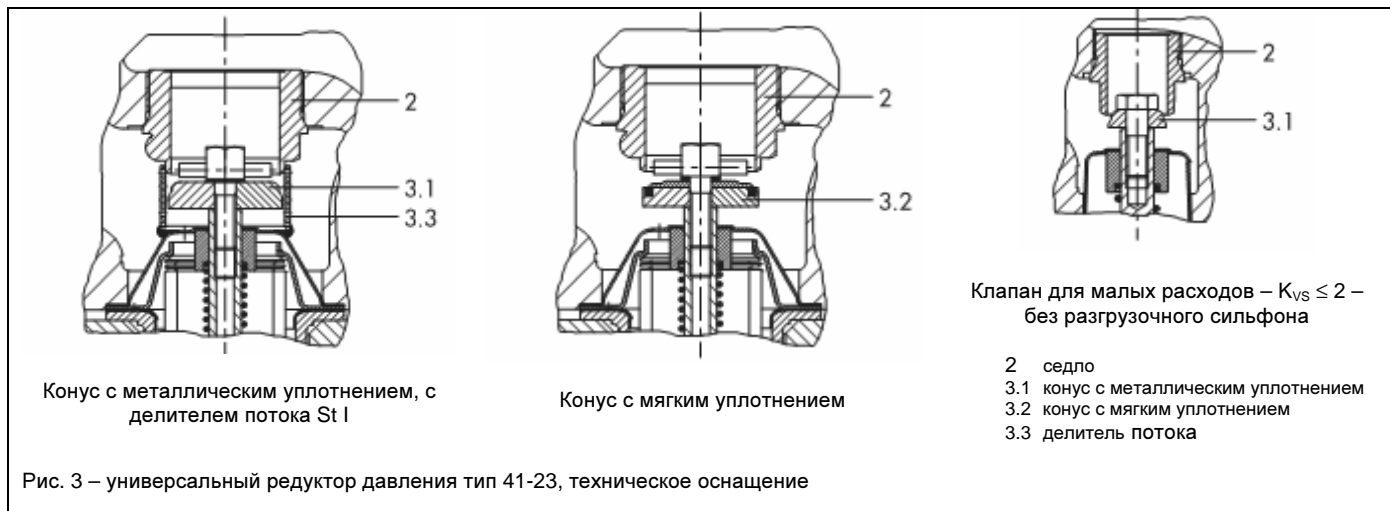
универсальный редуктор давления тип 41-23, техническое оснащение
